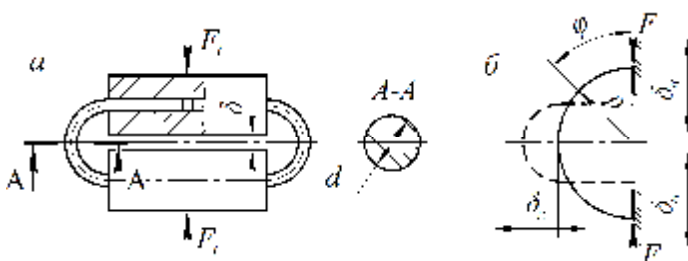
Конструктивна схема установки і розрахункова схема підковоподібних пружин
